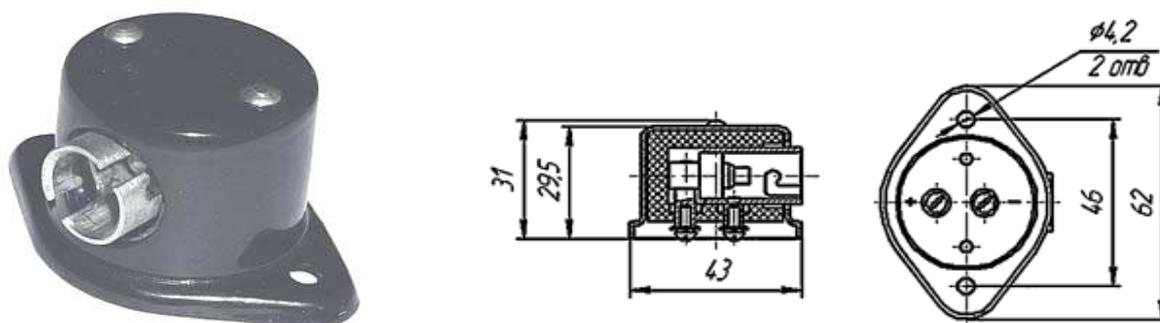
ШР-51, внешний вид и габаритные размеры
